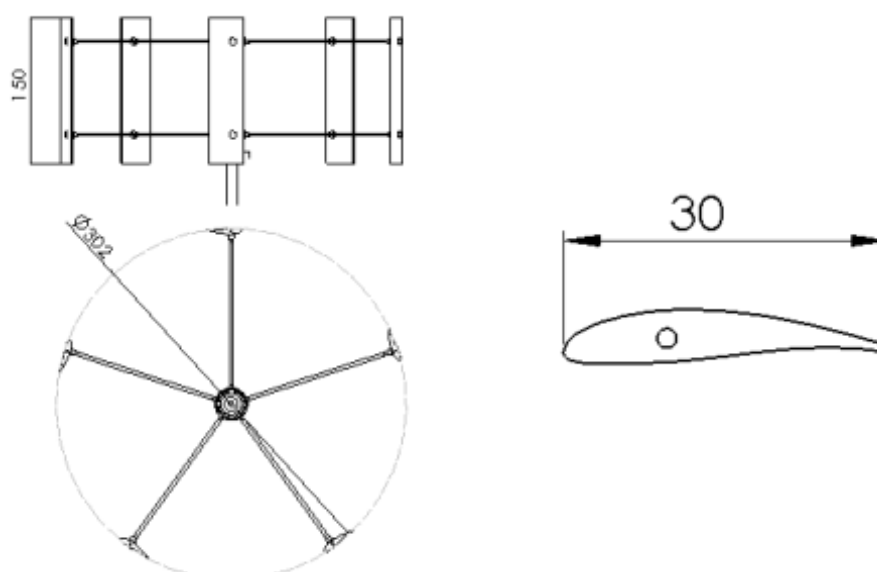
Dimensões do rotor da turbina em mm. Fonte: Fiabani (2016).
